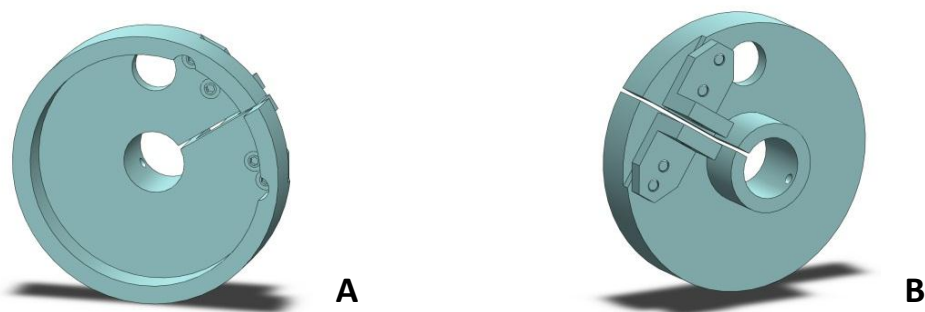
Peça de fixação do Hélice: a) vista posterior; b) vista anterior.
